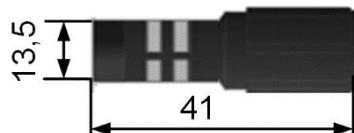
Внешний вид и габаритные размеры укороченного микрофона
